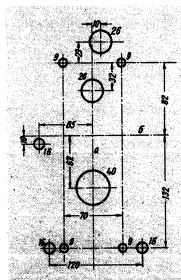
Сверление отверстий для установки на изоляционных плитах контакторов типа КП 524 и КП 534 с задним присоединением
